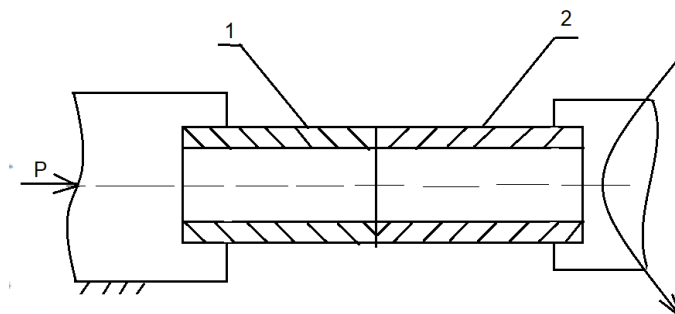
Торцева схема кільцевих зразків: 1 – нерухомий зразок; 2 – рухомий зразок.
